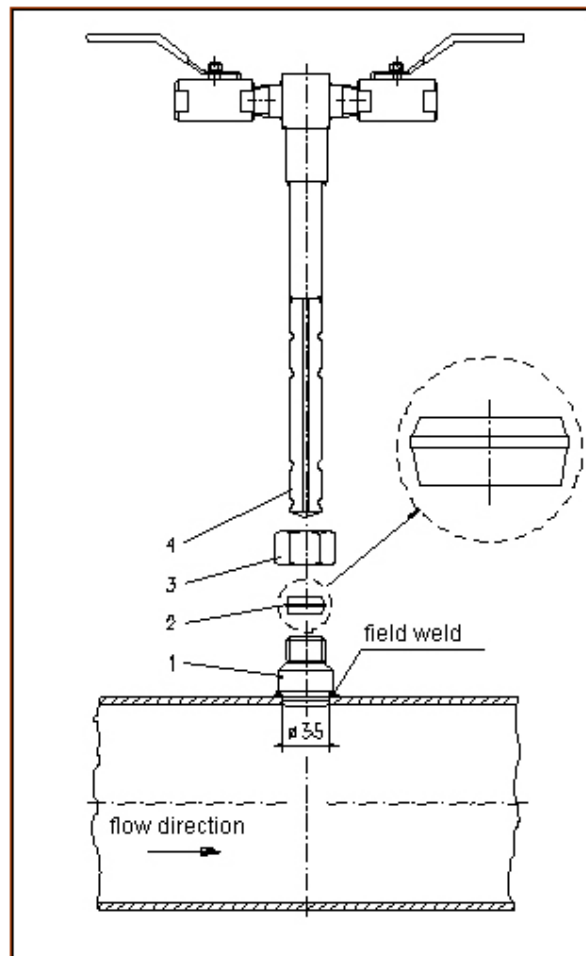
Montage einer IBR ohne Gegenlager (IBR-20/25/35)
